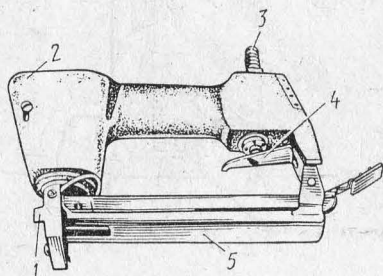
Пневматический пистолет: 1 — ударник, 2 — корпус, 3 — штуцер, 4 — курок, 5 — кассета со скобами
